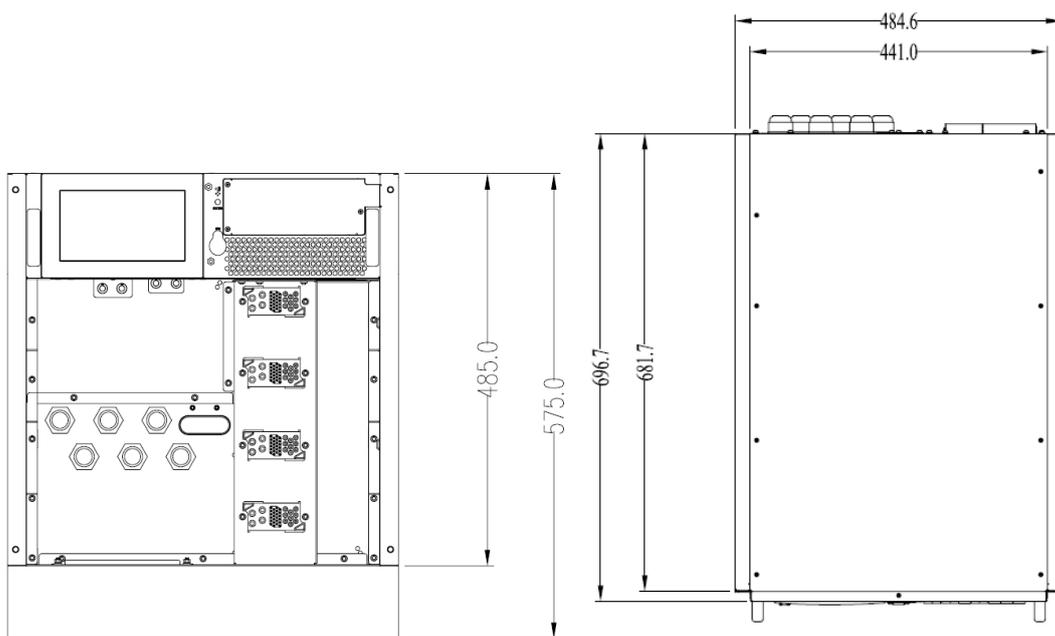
Габаритные размеры 3 и 4-модульного ИБП
